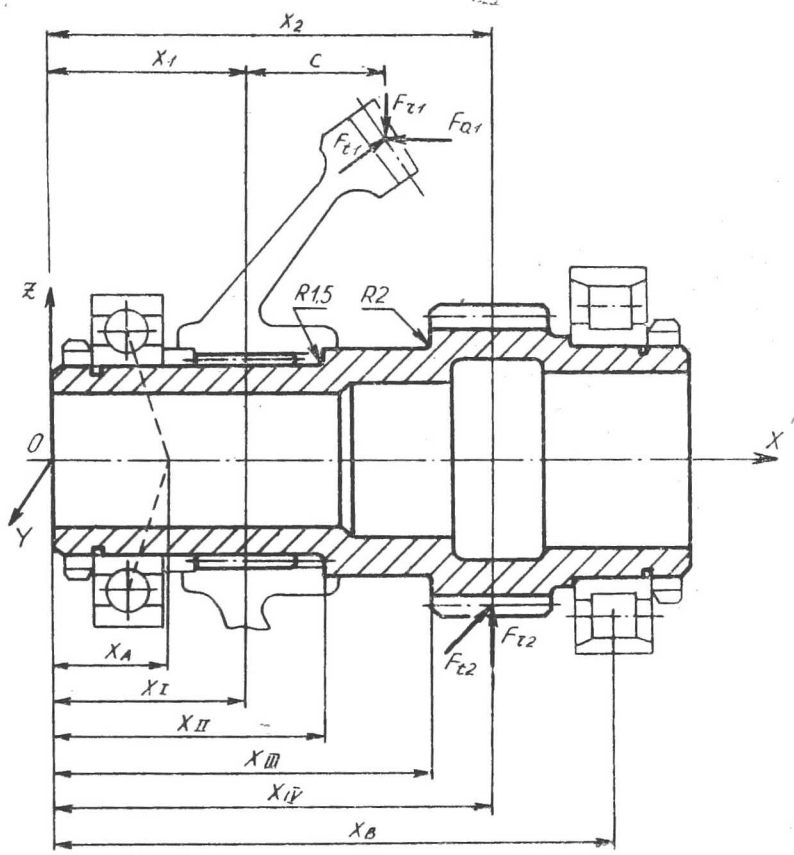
Эскиз и расчетная схема промежуточного вала редуктора
